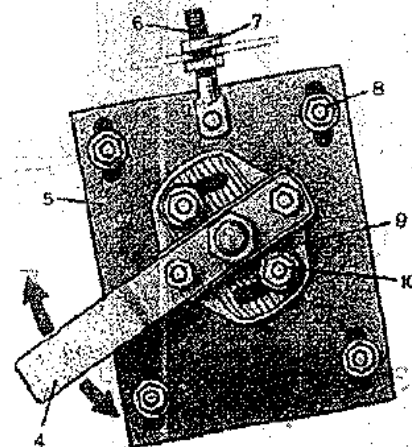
Схема механизма регулирования шнека: 4 - рычаг; 5 - плита; 6 - винт; 7, 8, 10 - гайки; 9-сбойма
